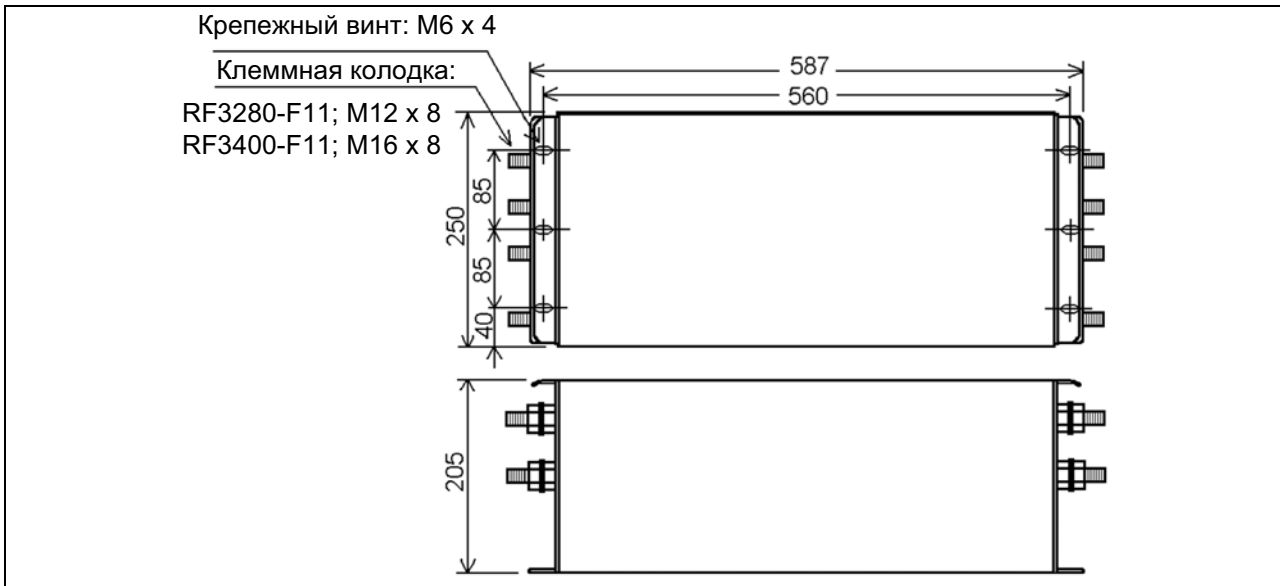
Габаритные размеры (RF3280-F11, RF3400-F11)
